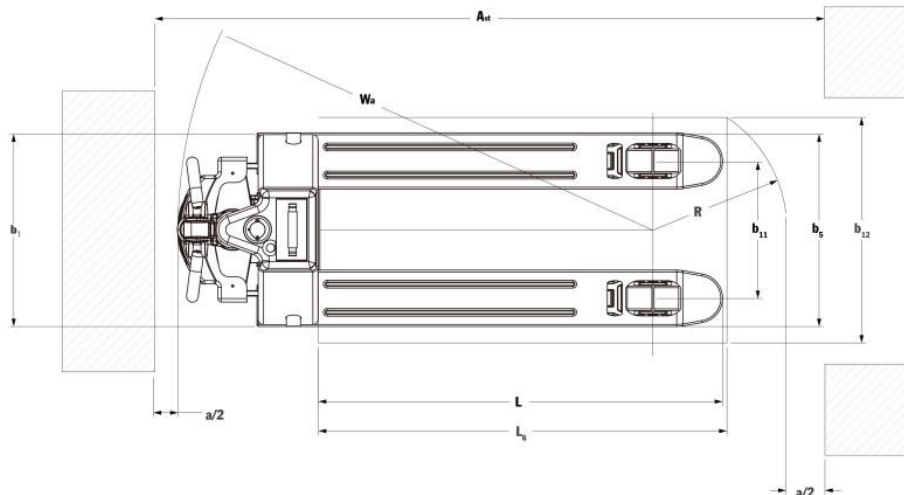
Diagrama de dimensões. Vista em planta e raio de viragem.
